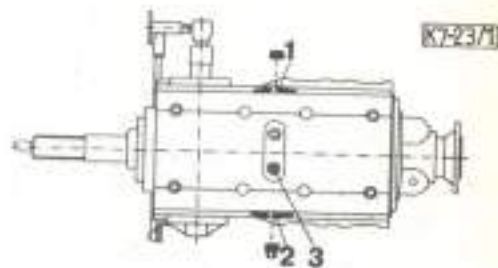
Коробка передач типа ZF 56-90M (K7-23/1)
